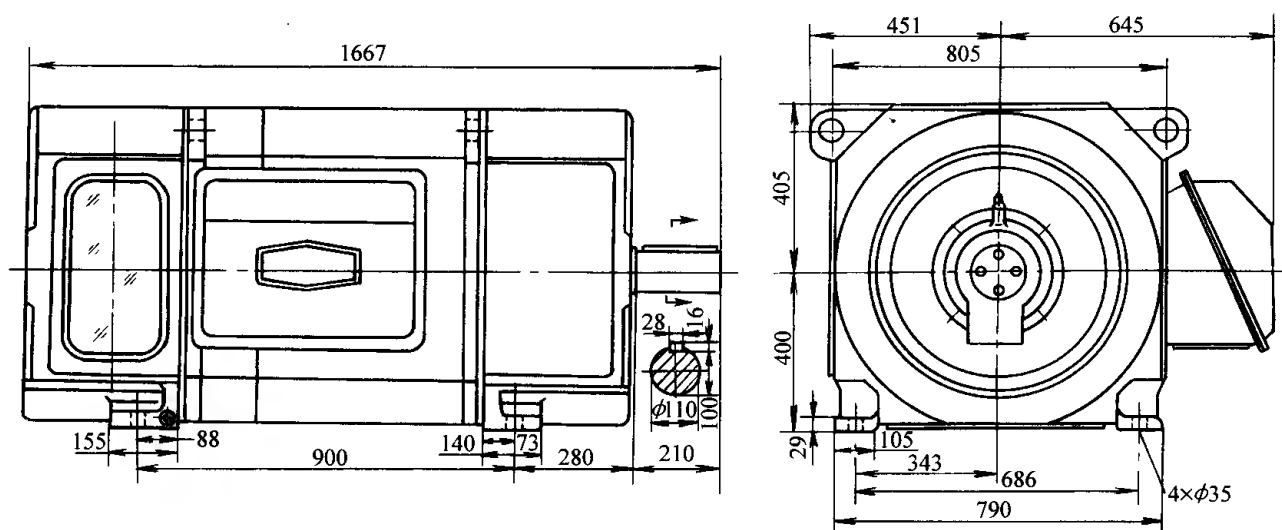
ZD3-400L1 型 160kW 440V 320/1200r/min IC37 直流电动机安装及外形尺寸图
